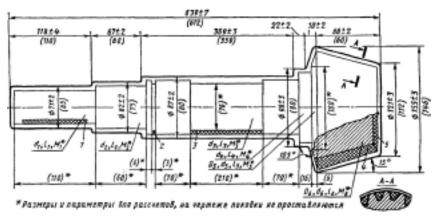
Чертеж на поковку детали вал-шестерня
